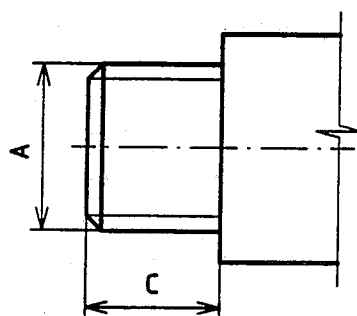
Einzelansicht des Zulaufgewindes des Aufputz-Auslaufventils für Wandmontage
